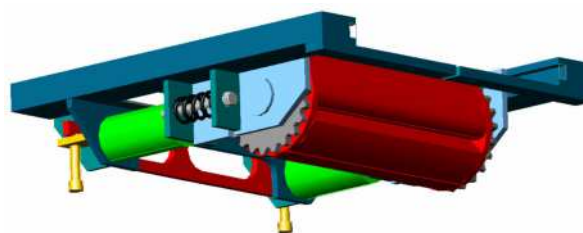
Il dispositivo di tensionamento dell'FRP (visto dalla testata della trave)
